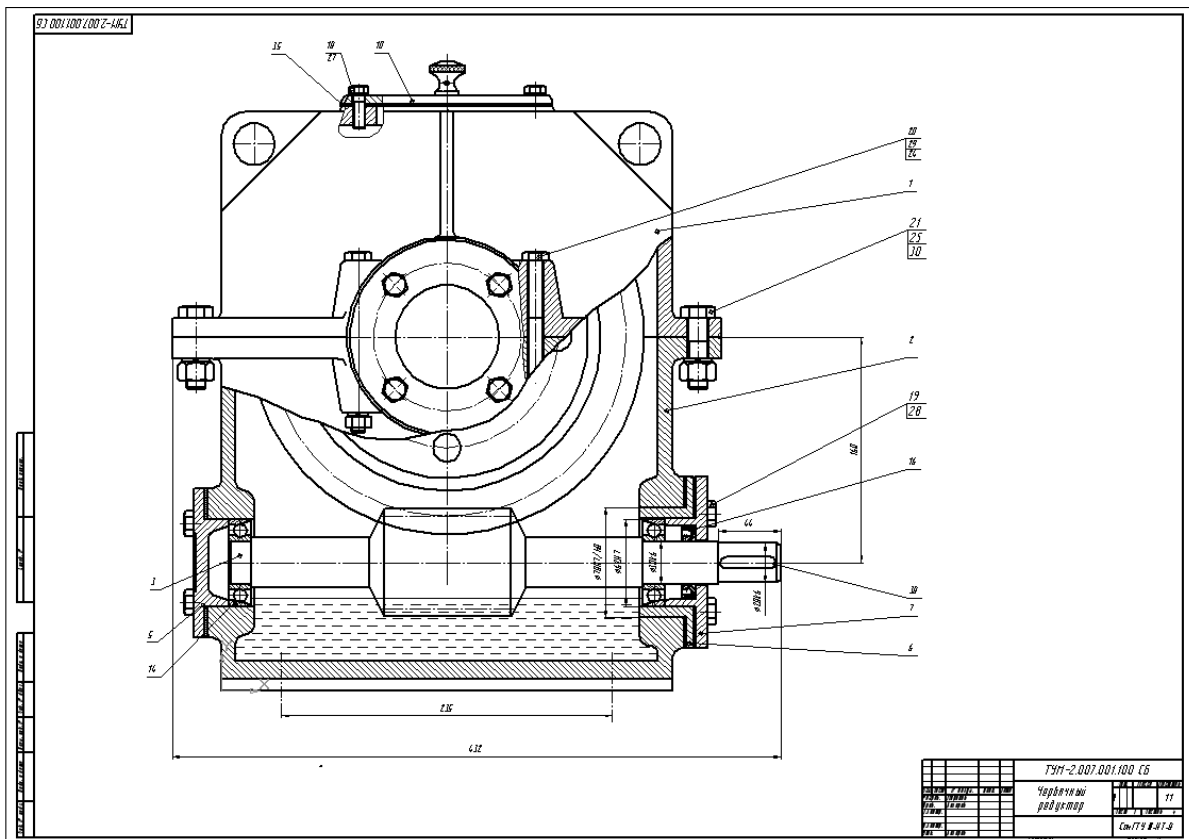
Пример сборочного чертежа червячного редуктора (главный вид)
